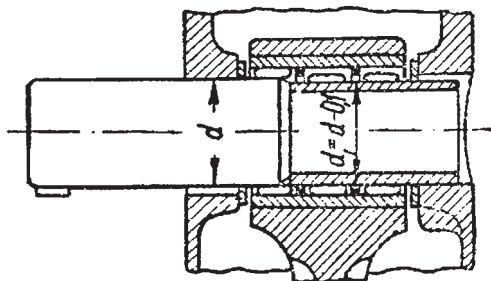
Монтаж игольчатого некомплектного подшипника
